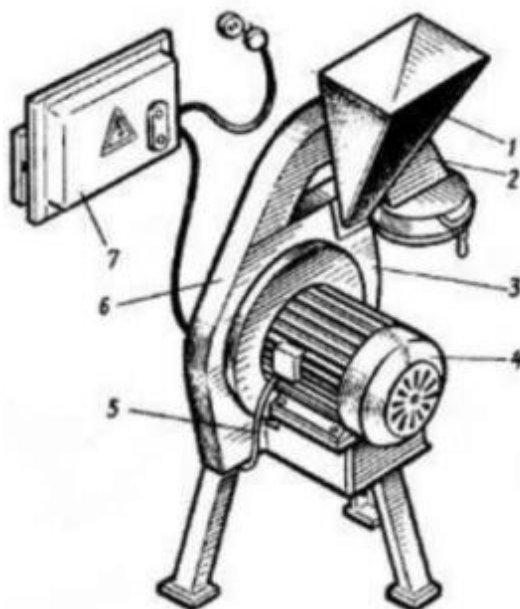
Дробарка зернова ДЗ-Т-1
